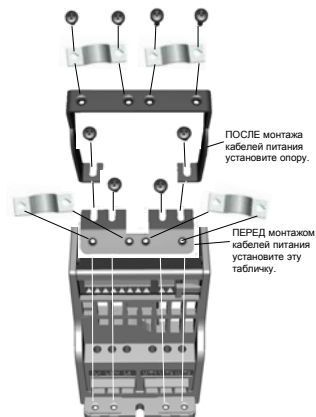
Установка заземляющей пластины и кабельных опор API, типоразмеры MI1–MI3
